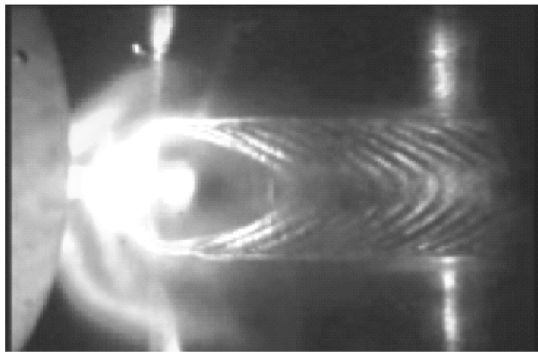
TIG 填丝自动焊管的焊缝成形
